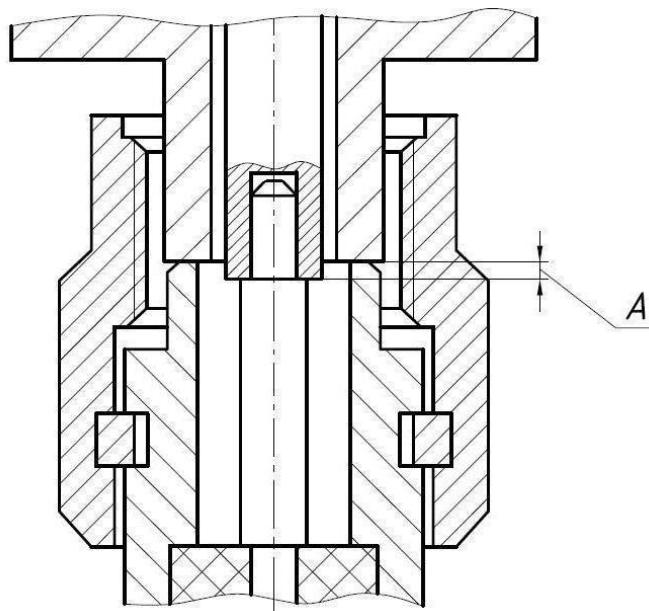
Проверка размера «A» соединителя «вилка»
